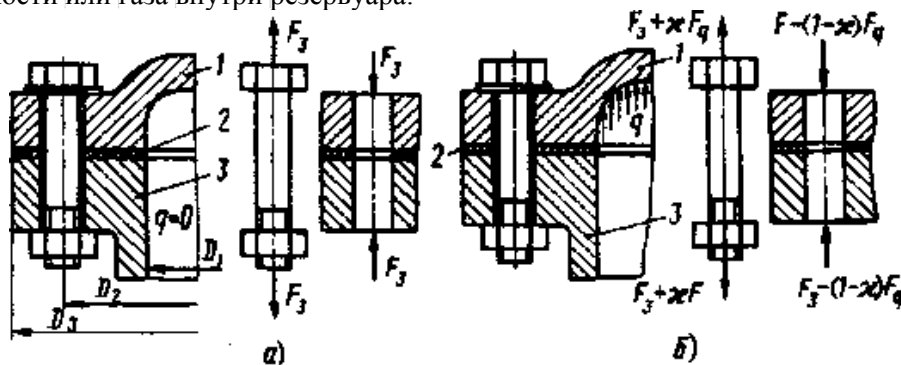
, Резьбовое соединение с затянутым болтом:
